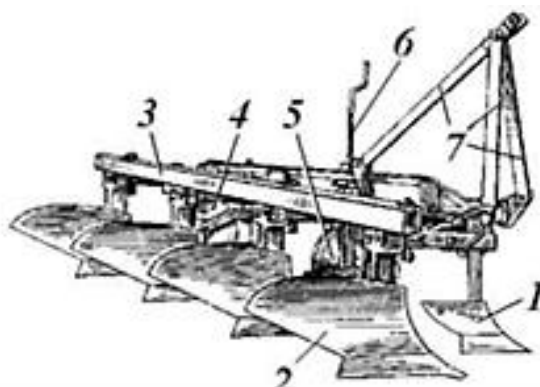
Плуг ПЛН-4-35: 1 – предплужник; 2 – корпус; 3 – рама; 4 – дисковый нож; 5 – опорное колесо; 6 – винтовой механизм регулирования глубины пахоты; 7 – навеска
